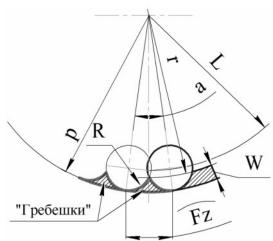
Волнообразная поверхность после фрезерования концевой фрезой
